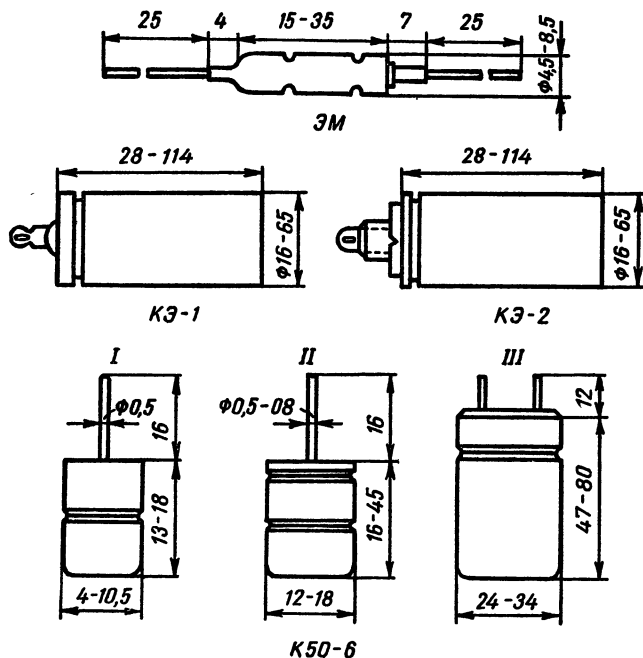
Габаритные чертежи электролитических конденсаторов.
